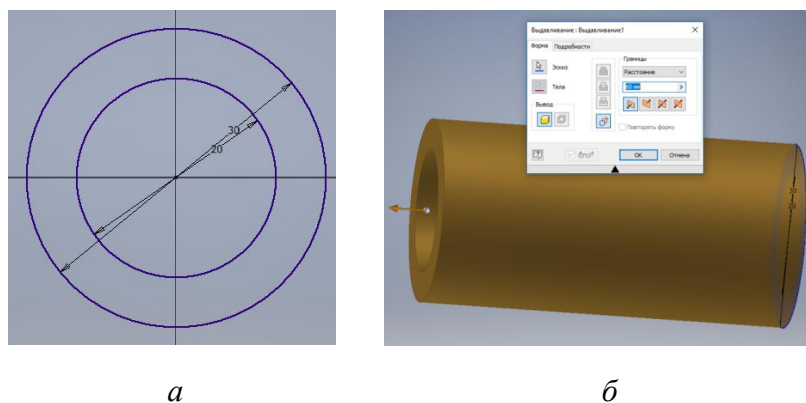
Эскиз (а) и 3D-модель (б) цилиндрического патрубка
